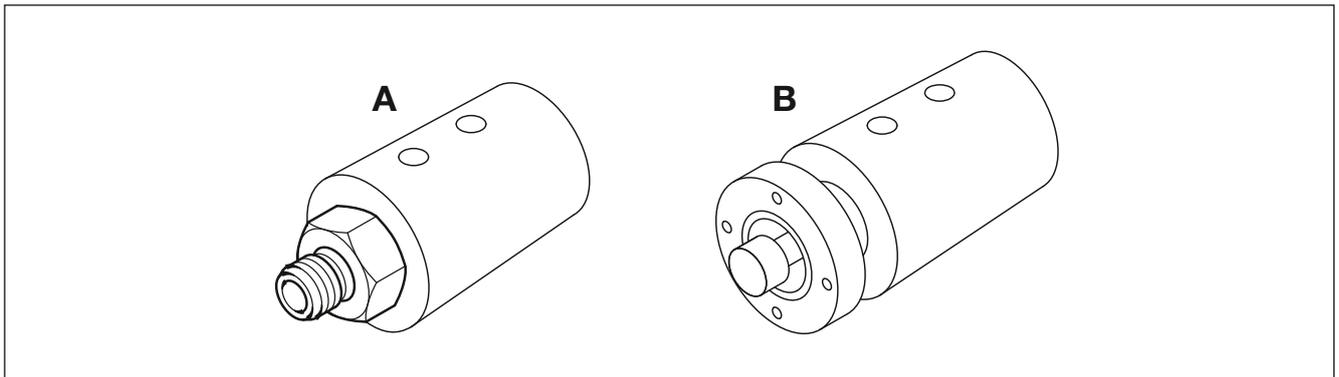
Variantes de fixation sur l'arbre de la machine
